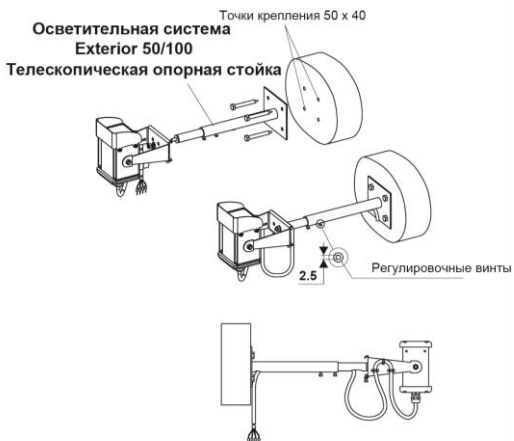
Крепление на опорную стойку осветительной системы Exterior 50
